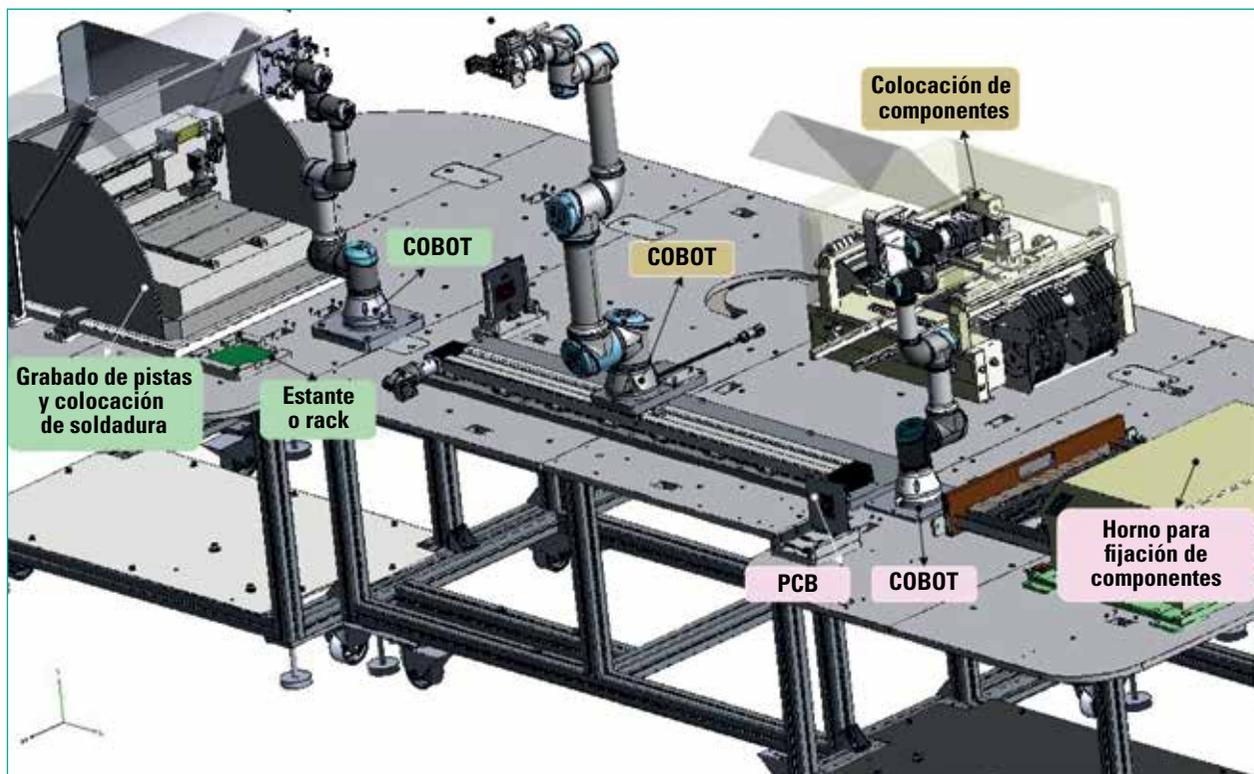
Celda de manufactura de PCB instalada en LANITED. Imagen elaborada por los autores.
